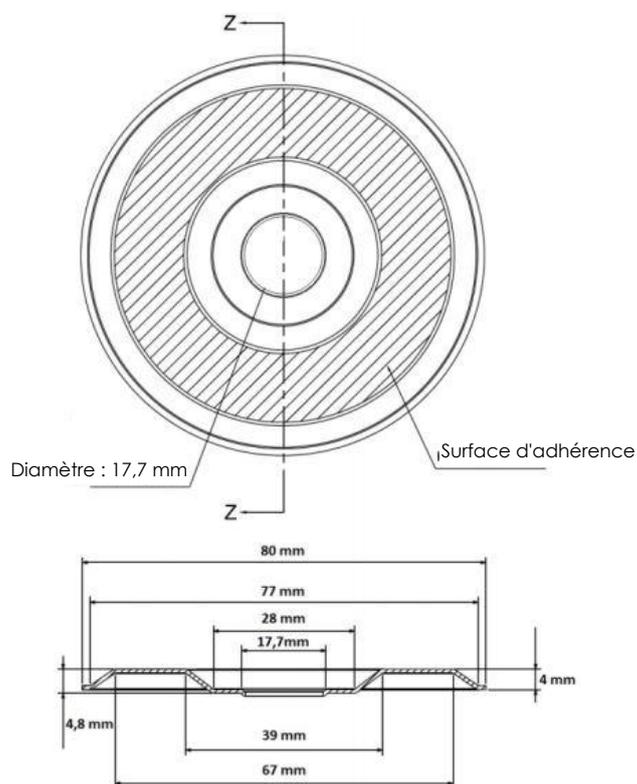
plaque OMG RHINOBOND TREADSAFE PLATE (au-dessus) + vis OMG XHD (Extra Heavy Duty) (en dessous) + cheville OMG TREADSAFE (en dessous)
